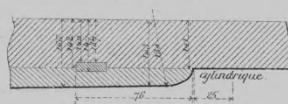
Assemblage de la jaquette et de la frette tourrillons en a.
